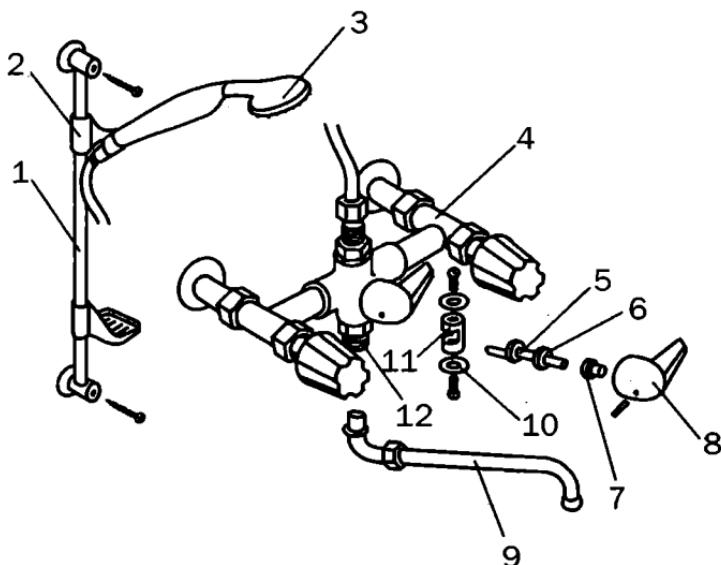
Конструкция смесителя с золотниковым переключателем «душ — излив»: 1 — штанга; 2 — держатель; 3 — душевая сетка; 4 — корпус; 5 — кривошип; 6 — уплотнение; 7 — винт; 8 — рукоятка; 9 — излив; 10 — прокладка; 11 — золотник; 12 — переходник
